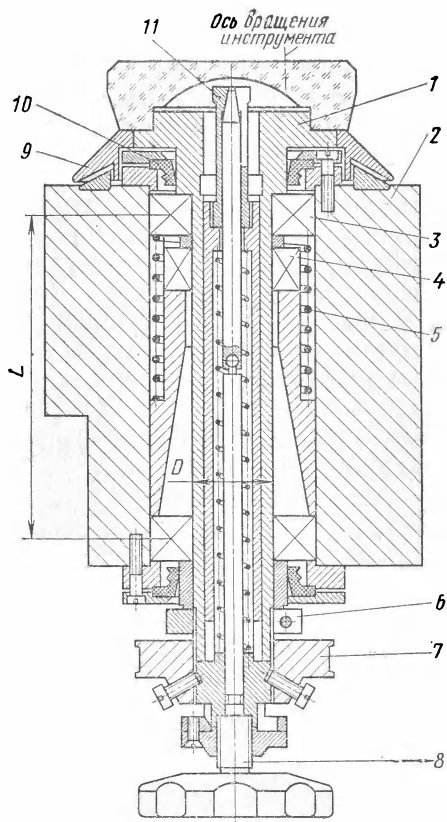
Нижний шпиндель плоскоповодочного станка:
